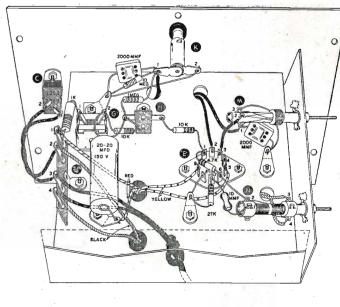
Vista del telaio del generatore di barra con la disposizione dei vari componenti e del cablaggio. E' una altra illustrazione che accompagna il manuale d'istruzione per il montaggio.
